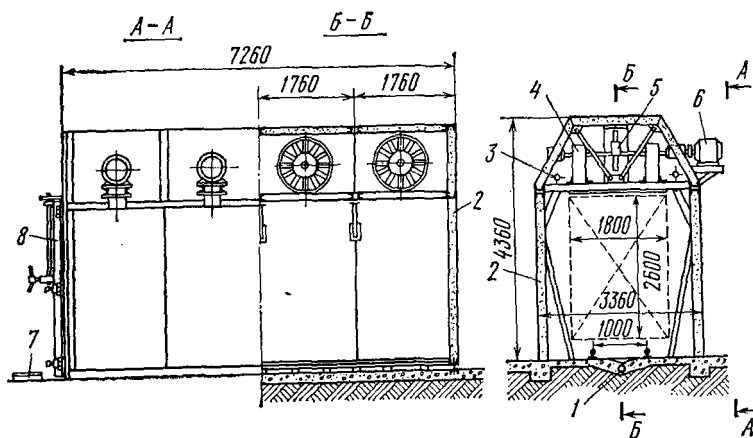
Сборная металлическая сушильная камера Гипродревпрома СПВ-62:
